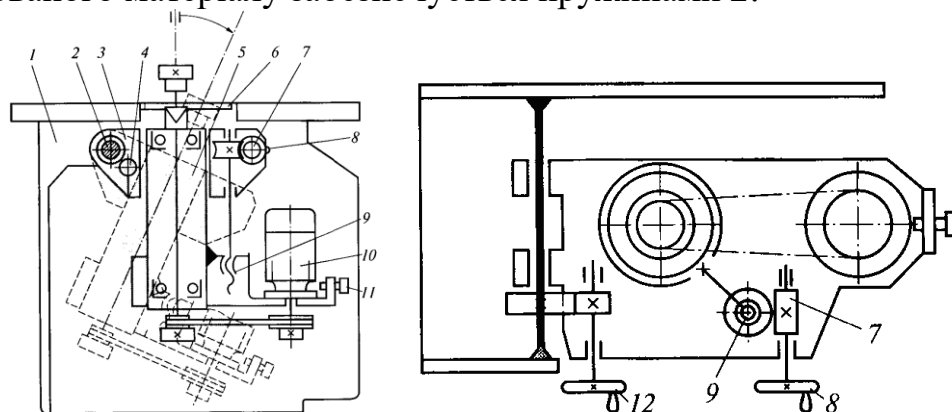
Фрезерний верстат з нахильним супортом: 1 – станина; 2 – скалка; 3 – супорт; 4 – зубчаста передача; 5 – шпиндельний блок; 6 – заглушка; 7 – черв'як; 8, 12 – маховички; 9 – гвинтова передача; 10 – електродвигун; 11 – гвинт натягу ремня
